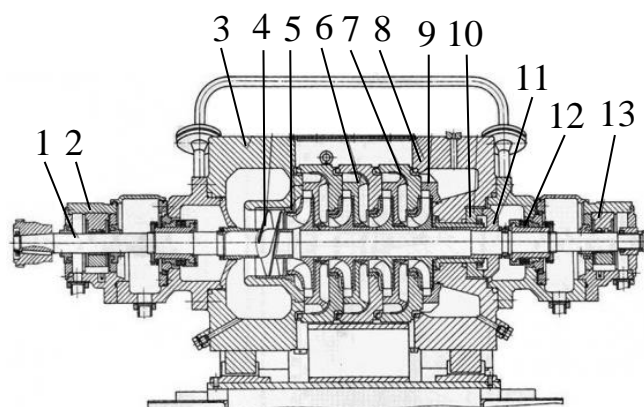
Многоступенчатый магистральный насос: 1 – вал; 2 – корпус; 3 – крышка корпуса; 4,5 – втулки вала; 6 – рабочее колесо; 7 – кольцо уплотняющее; 8 – узел уплотнения вала; 9 – подшипник скольжения; 10 – радиально-упорный подшипник.
